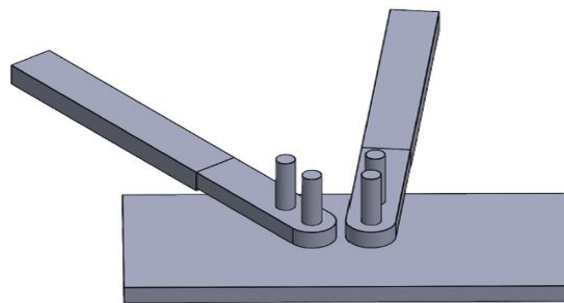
Ensamble de la máquina dobladora de eslabones de cadena.
